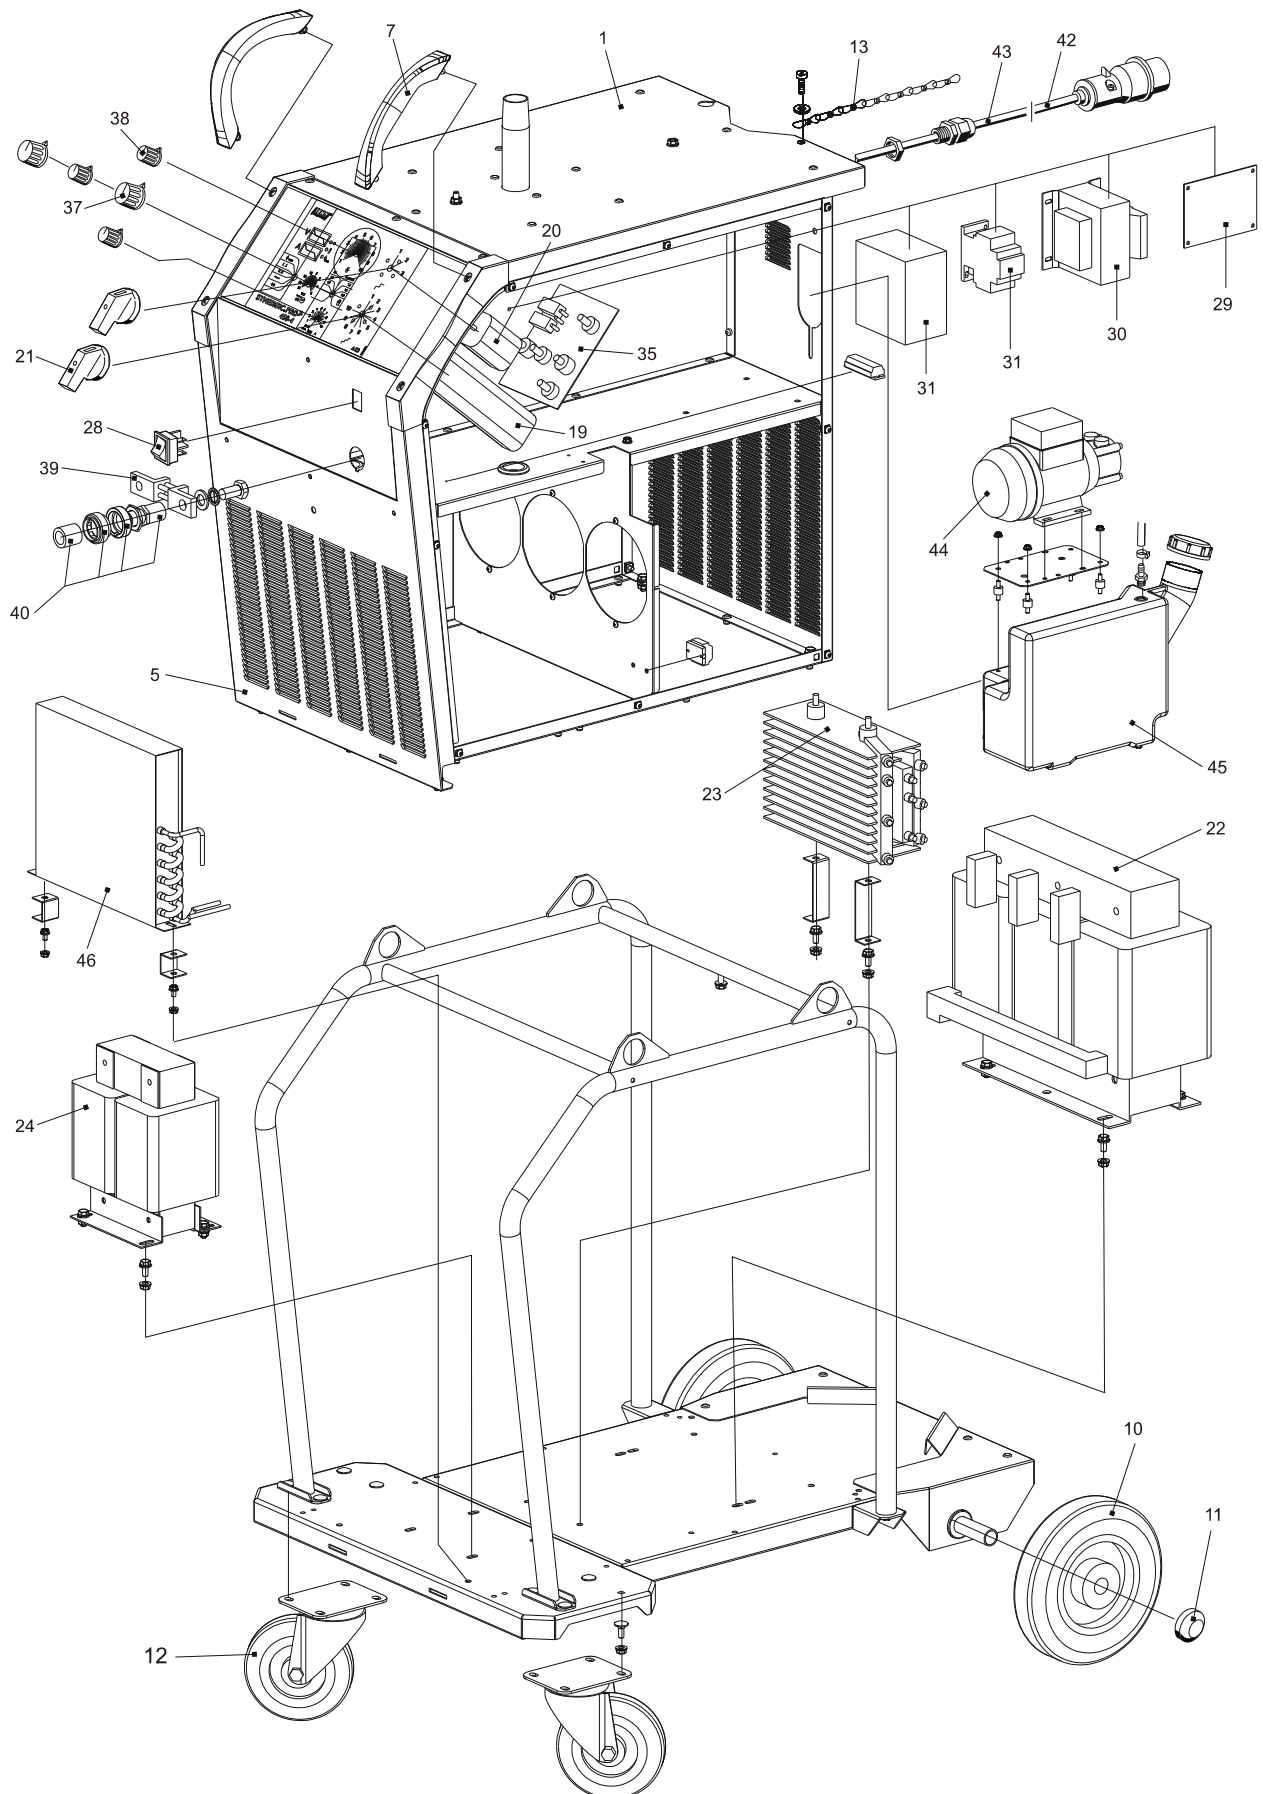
Explosionszeichnung SYNERGIC.PRO² 500-4WS – 600-4WS (rechts)
